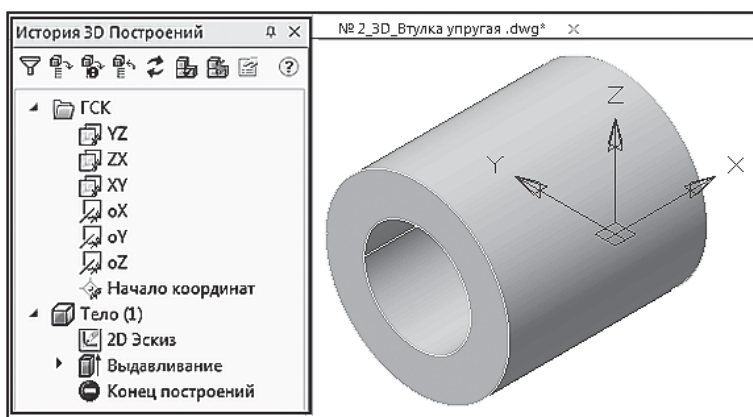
3D-модель детали № 2 «Втулка упорная»
